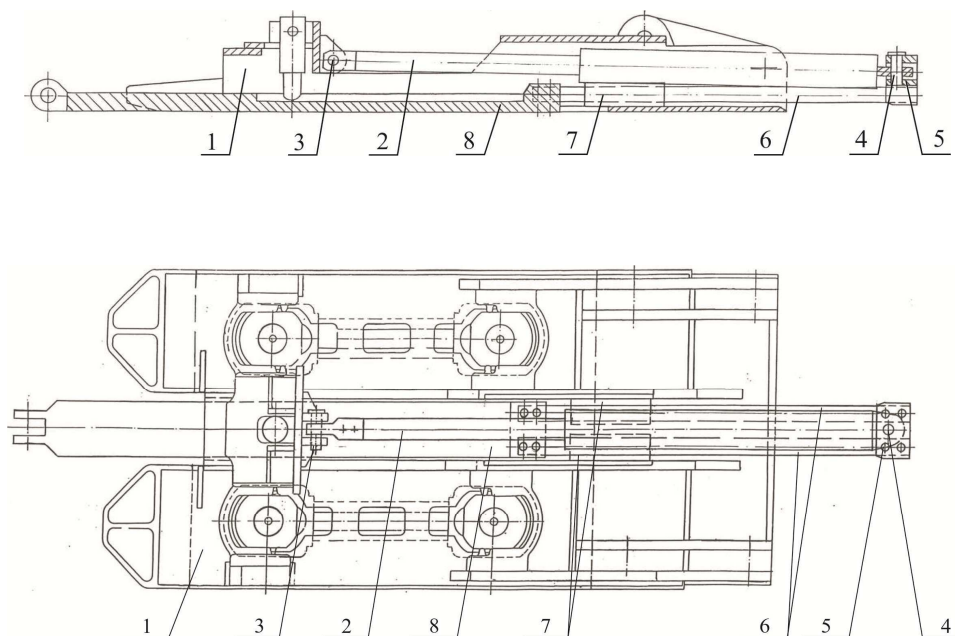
Устройство для передвижки секции механизированной крепи и перемещения забойного конвейера струговой установки (механизм передвижки)
